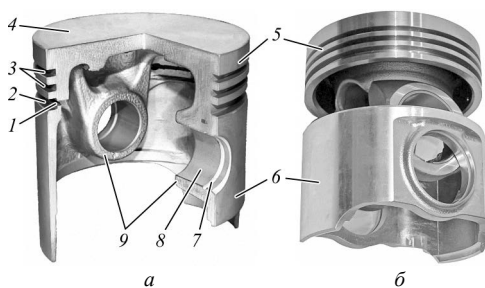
Поршень: *а* – цельный; *б* – составной; 1 – отверстия для слива масла; 2 – канавка под маслосъемное кольцо; 3 – канавка под компрессионное кольцо; 4 – днище; 5 – головка; 6 – юбка; 7 – канавка под стопорное кольцо; 8 – отверстие под поршневой палец; 9 – бобышка
